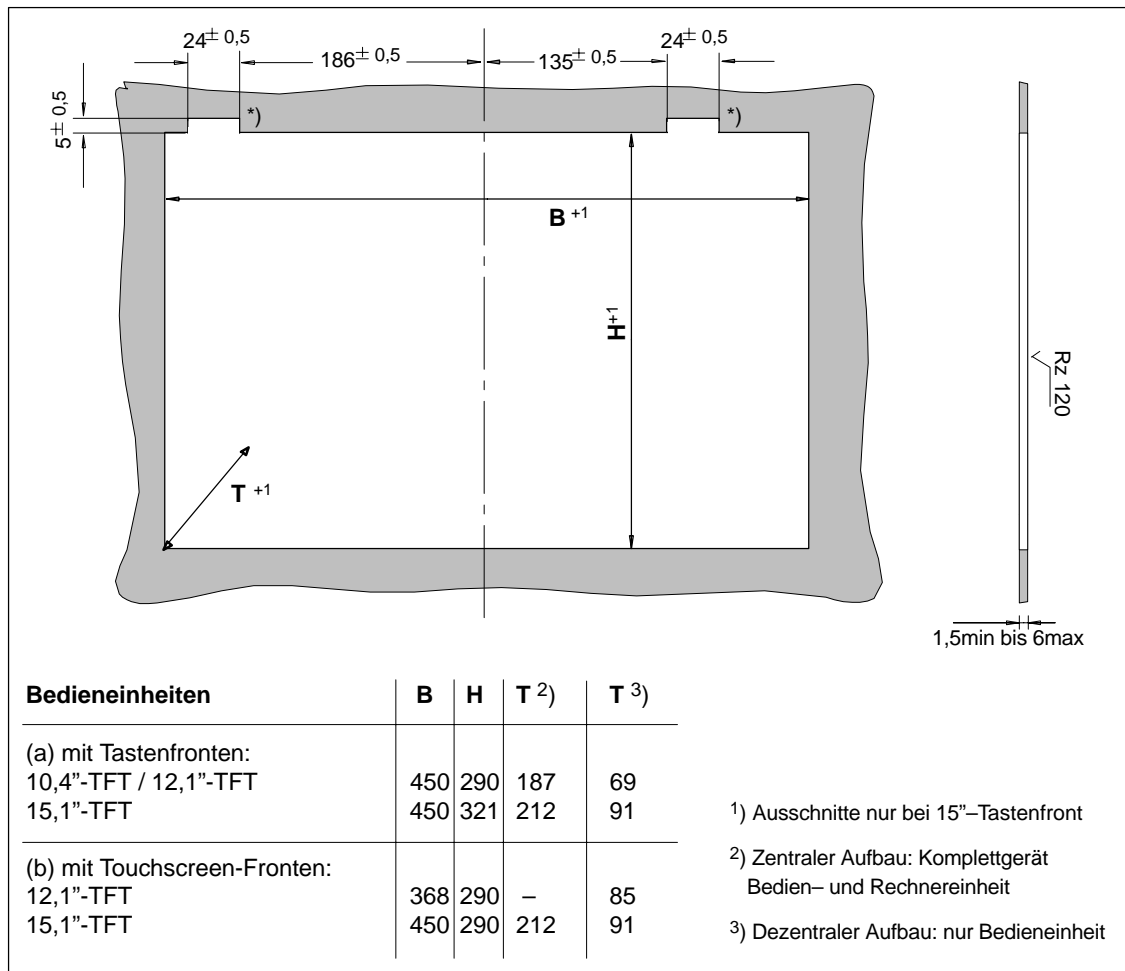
Einbauausschnitt für Standardeinbau Panel PC 870 (Angaben: Breite x Höhe x Tiefe in mm)
